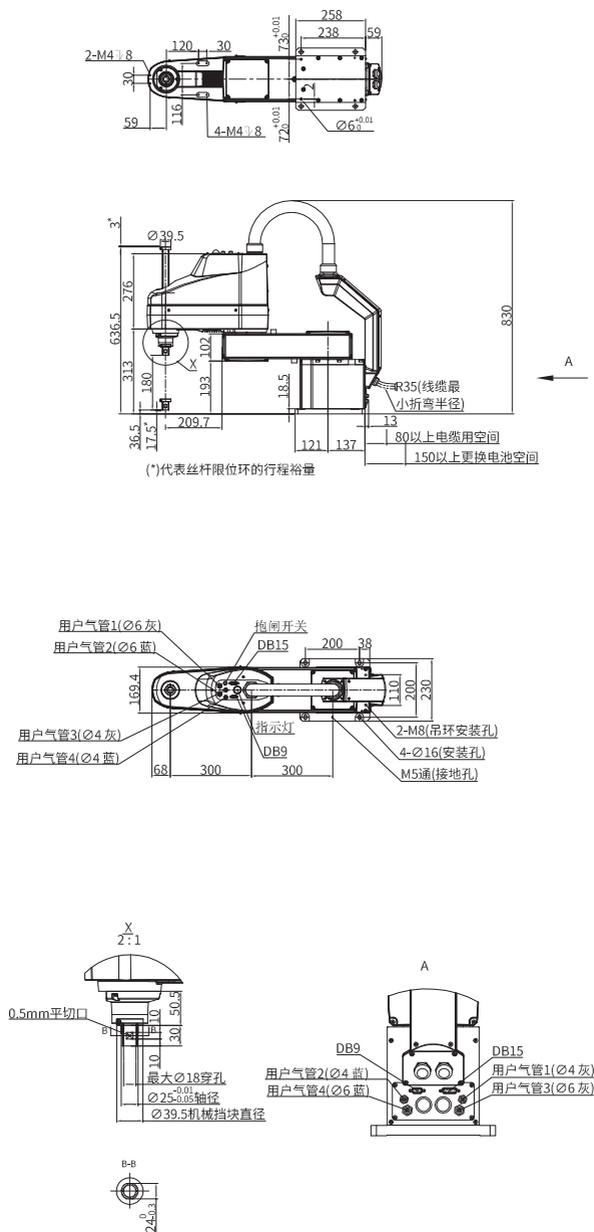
IRB111-20-60Z18TS3 安装尺寸
